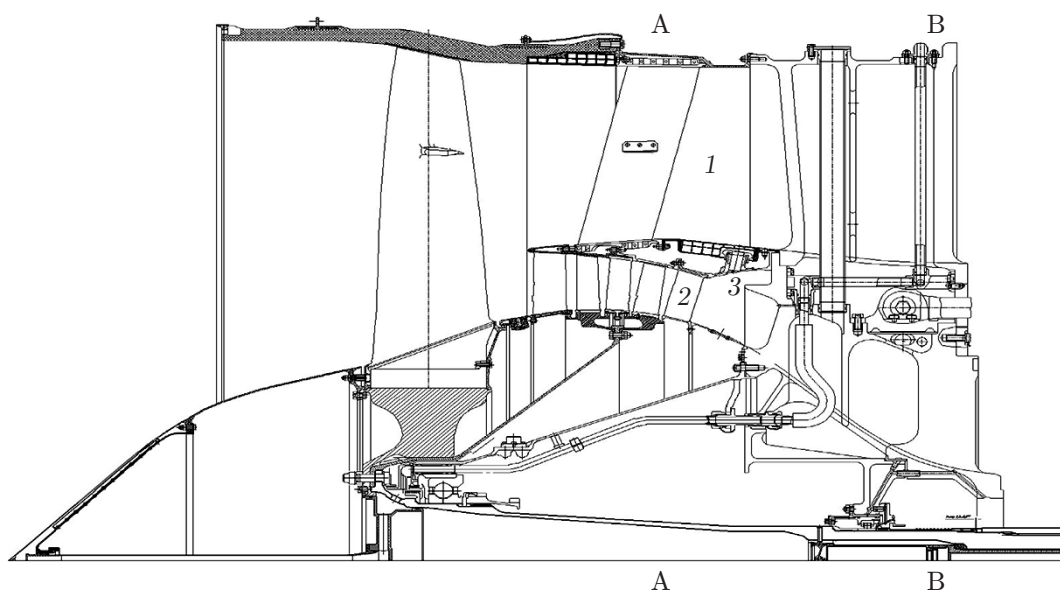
Схема компрессора низкого давления двигателя ПС-90А:
